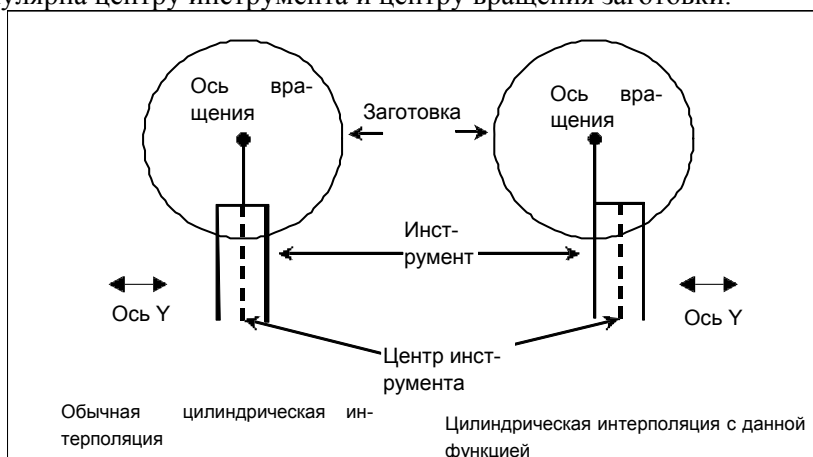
(а) Сравнение с обычной цилиндрической интерполяцией
